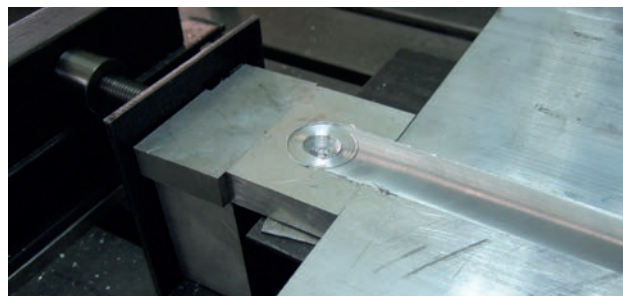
Накладная пластина в конце сварочного шва
